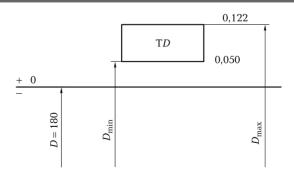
Схема расположения поля допуска для номинального размера отверстия 180 мм
